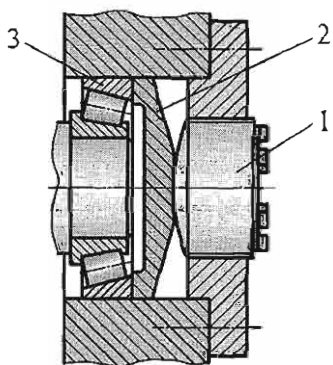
Осевое перемещение вала с червячным колесом винтами, установленными с обеих сторон вала
